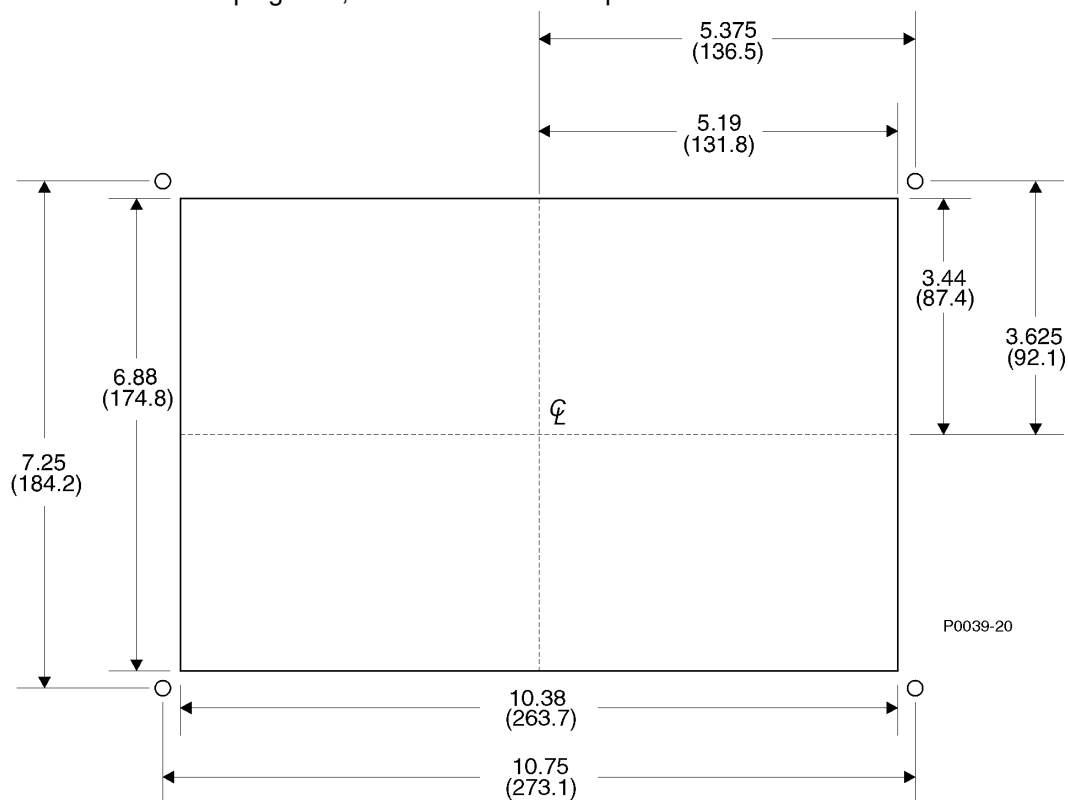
Dimensiones de Corte y Perforado del Panel
